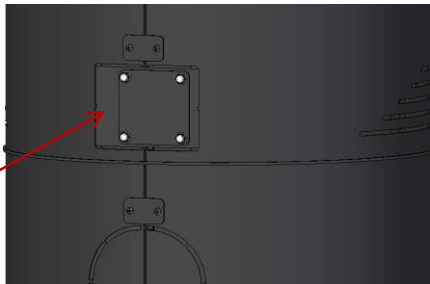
Vista posterior do equipamento, (M) secção a eliminar para entrada de ar externa
